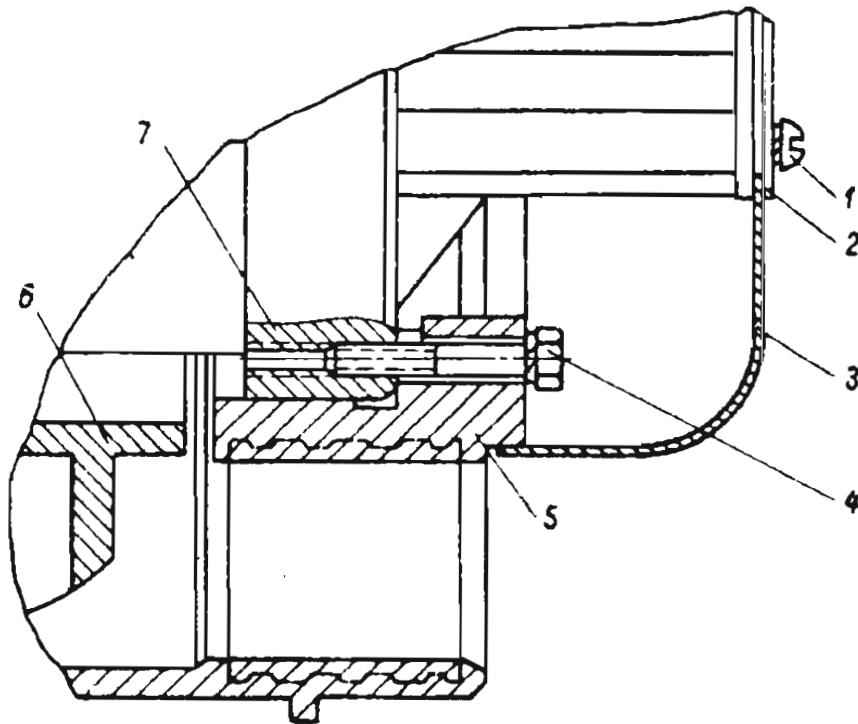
Befestigung der Lichtmaschine am Gebläseleitrad:
